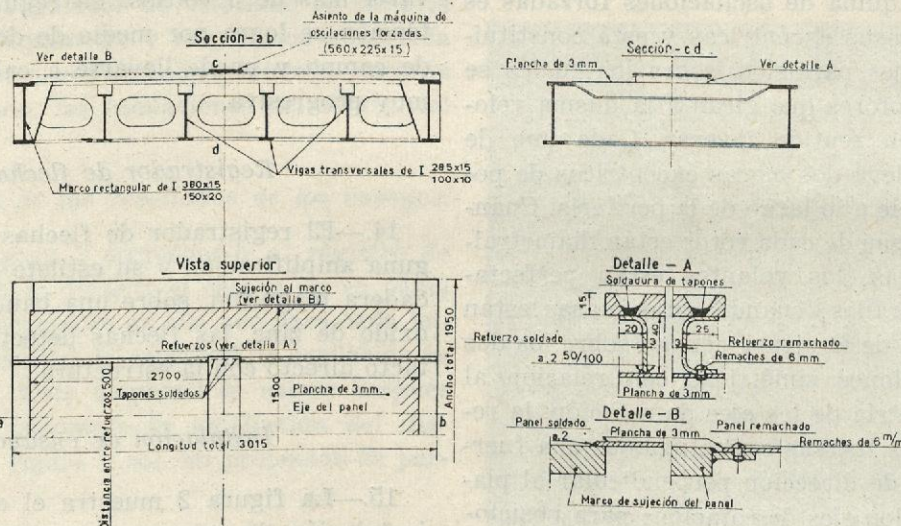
Paneles de ensayo remachado y soldado.
